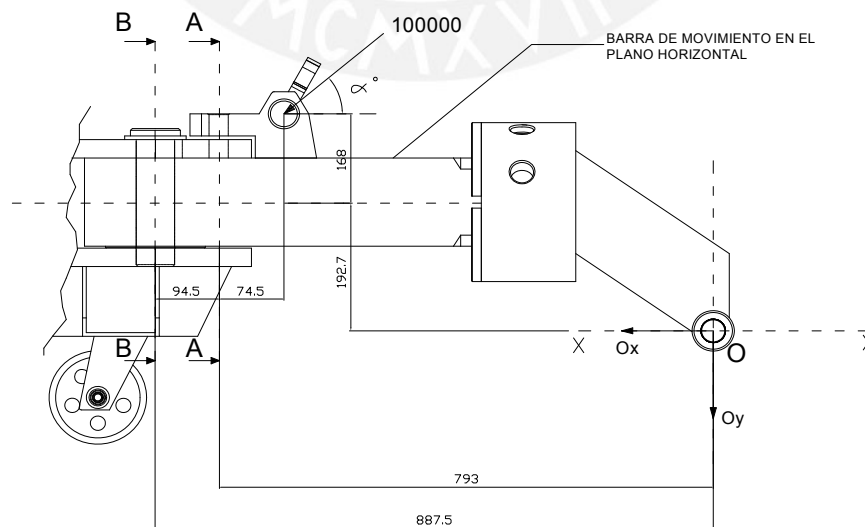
BARRA DE GIRO HORIZONTAL
